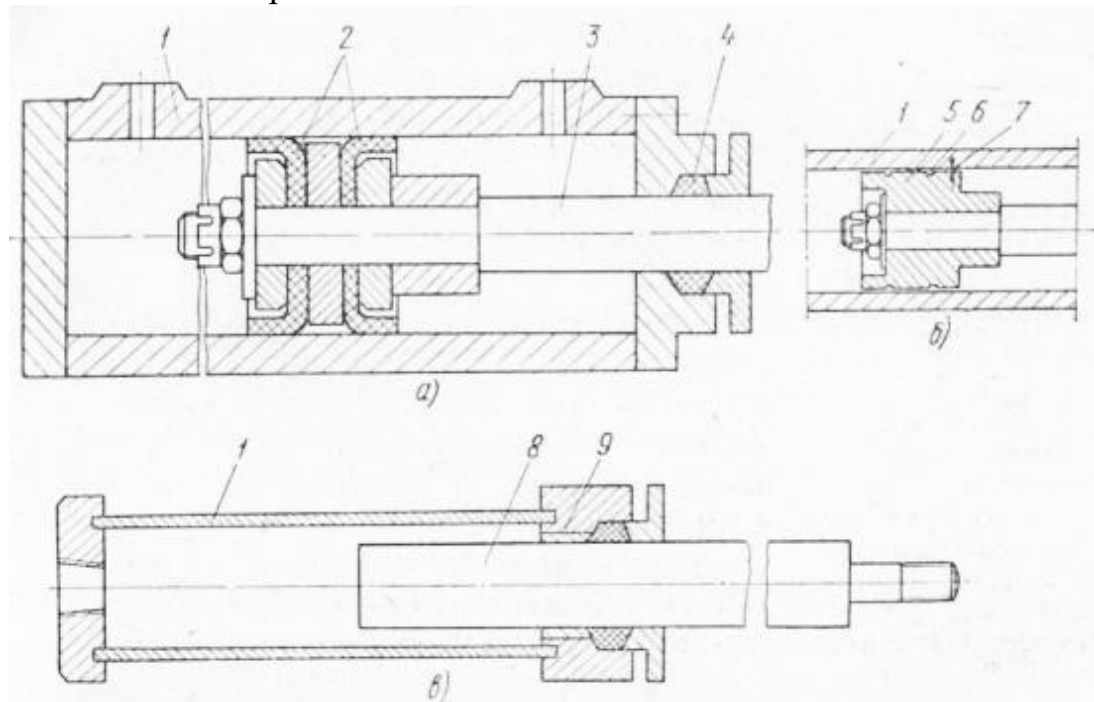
Цилиндры гидросистем и конструкции их поршней: а — цилиндр с поршнем, уплотненным манжетами, б — цилиндр с поршнем без манжет, в — цилиндр с поршнем плунжерного типа; 1 — цилиндр, 2 — манжеты, 3 — шток, 4 — уплотнение штока, 5 — поршень, 6 — канавки для уравнивания давления по окружности поршня, 7 — зазор, 8 — плунжер, 9 — втулка
